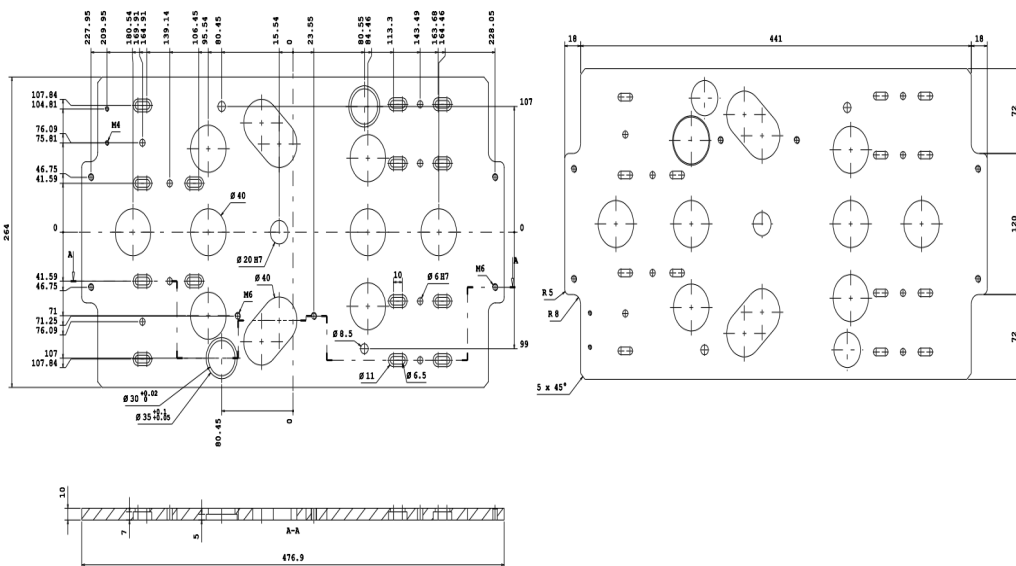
Planos 2D de la base donde se colocarán las molduras
